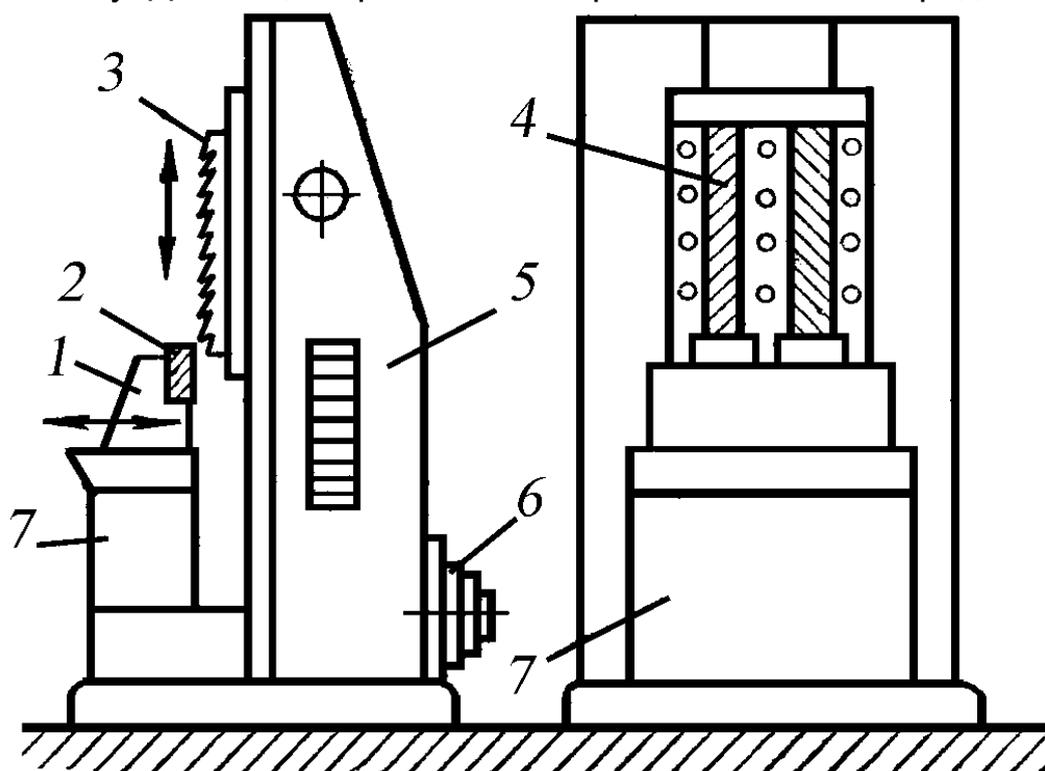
Схема вертикально-протяжного станка для наружного протягивания: 1 – суппорт; 2 – заготовка; 3 – подвижная плита; 4 – протяжки; 5 – станина; 6 – электропривод; 7 – стол
